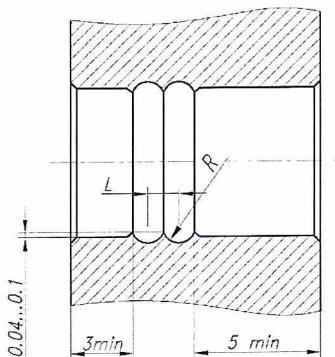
а – Двухрядный уплотнительный кольцевой рельеф
